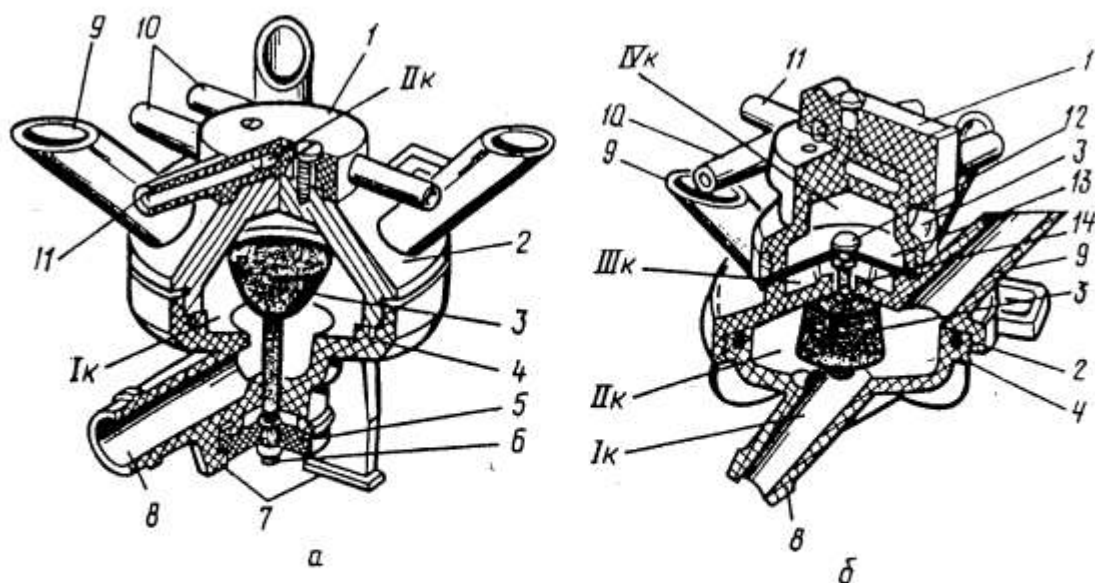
Коллектор АДУ-1 двухтактной (а) и трехтактной (б) модификаций: 1 — распределитель; 2 — корпус; 3 — клапан; 4 — корпус молокосборной камеры; 5 — шайба; 6 — шплинт; 7 — выступ-фиксатор; 8 — патрубок молочного шланга; 9 — молочный патрубок; 10 — патрубок переменного вакуума; 11 — штуцер; 12 — стержень; 13 — мембрана; 14 — канал
